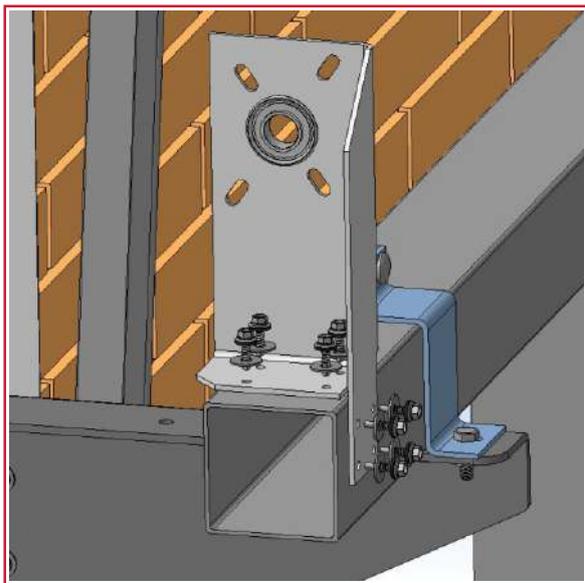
Крепление трубы к опорному кронштейну для низкого вала
